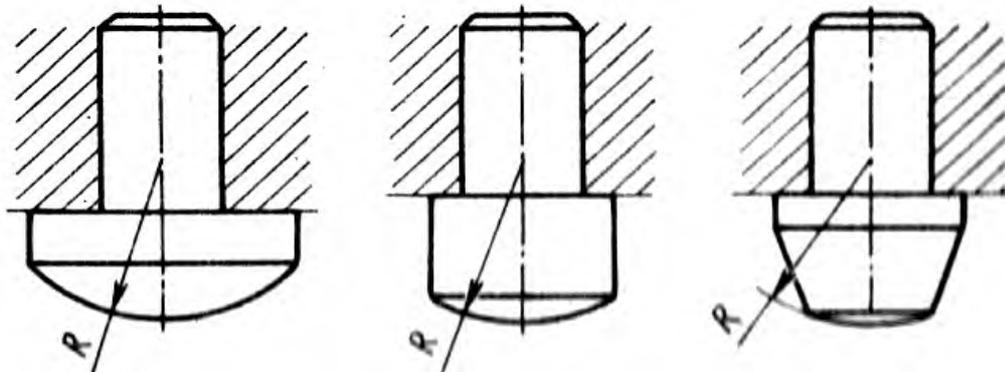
Сокращение рабочих размеров сферической поверхности
